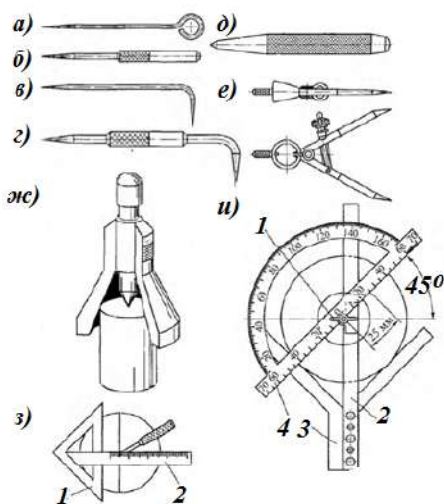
Чертилки: а - односторонняя с кольцом; б - односторонняя с ручкой; в - двухсторонняя; г - двухсторонняя с ручкой; д - кернер; е - циркуль пружинный; жс - колокол; з - угольник центроискатель; 1 - угольник; 2 - линейка; и - центрискатель-транспортир; 1 - стопорный винт; 2 - линейка; 3 - угольник; 4 - транспортир
